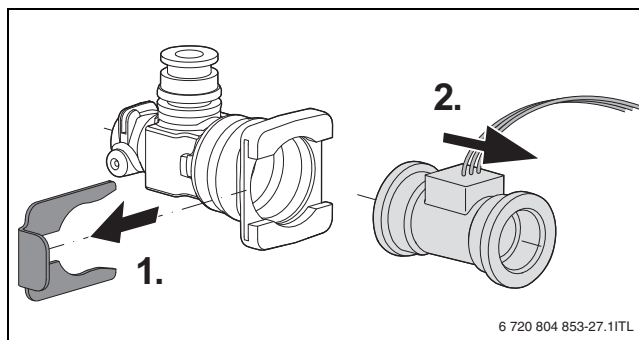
Demontați turbina de pe țeava pentru apă rece
